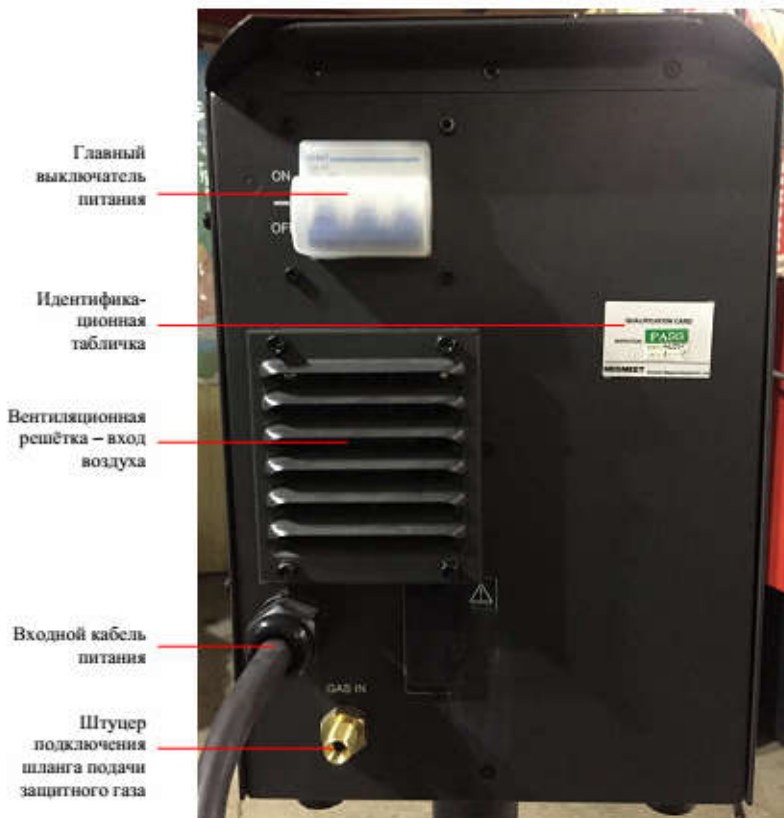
Задняя панель сварочного полуавтомата
